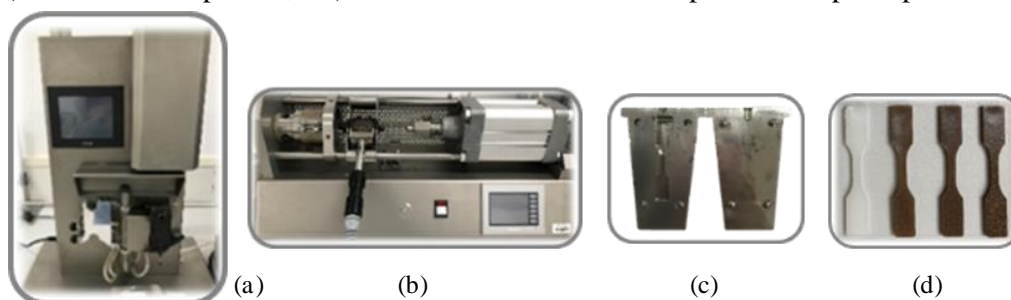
Equipamentos utilizados na fabricação dos corpos de prova: (a) Mini extrusora; (b) mini injetora; (c) molde; (d) corpos de provas fabricados.
